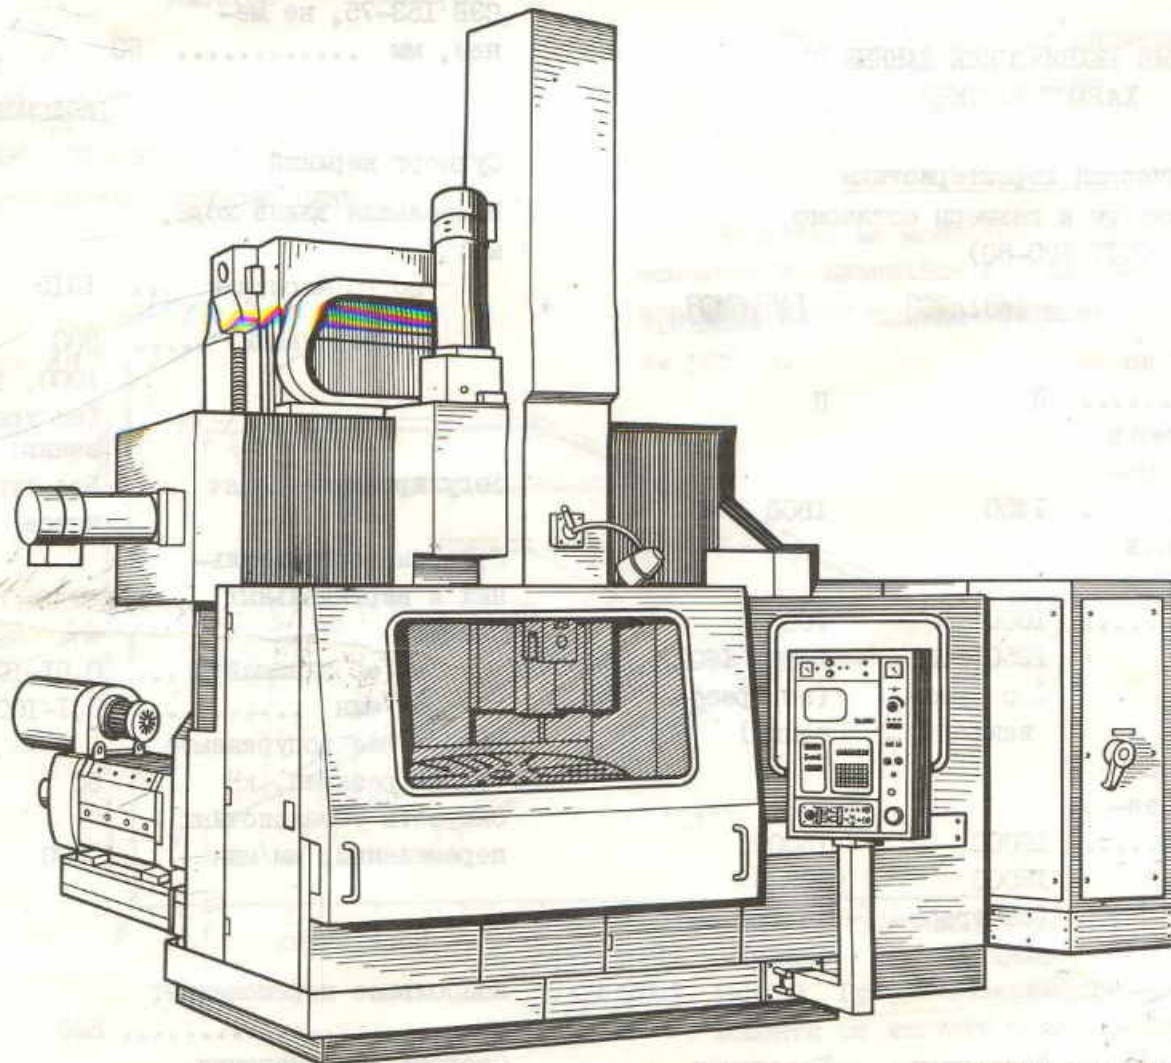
Станок токарно-карусельный одностоечный с ЧПУ
